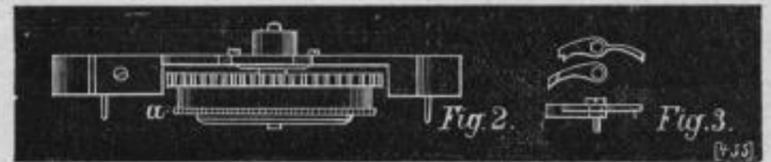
Seitenansicht des Federhauses; *a* das stählerne Sperrrad, welches erst aufgeschraubt wird, wenn das Federhaus samt Brücke auf der Platine befestigt ist. Fig. 3. Obere- und Seiten-Ansicht der Sperrkegel.
